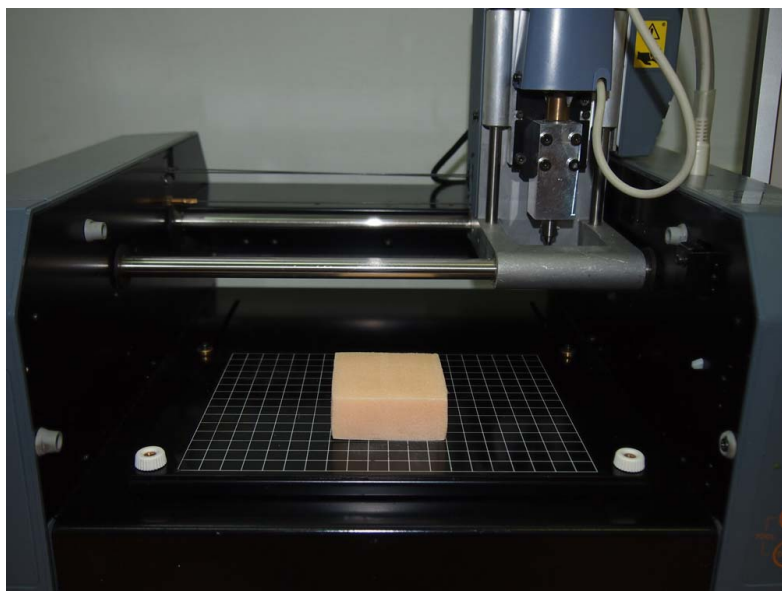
Рабочая зона станка с установленной заготовкой
